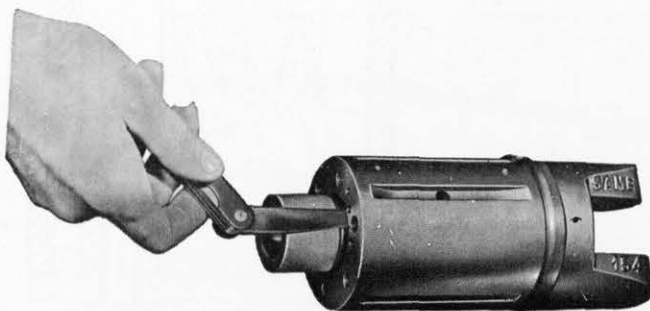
Spielmessung zwischen Steuergerät und Kolben mit dem Dickenmesser 5.9030.270.0.
